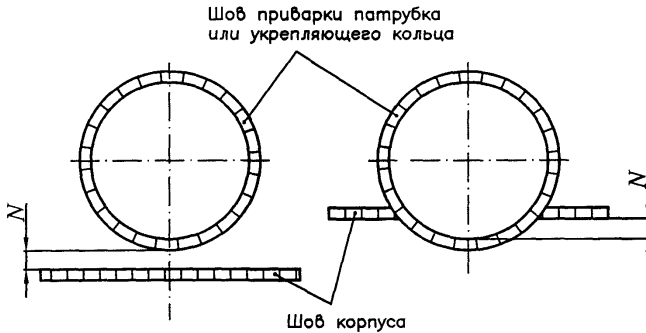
Схема определения расстояния между краем шва корпуса и краем шва приварки детали
